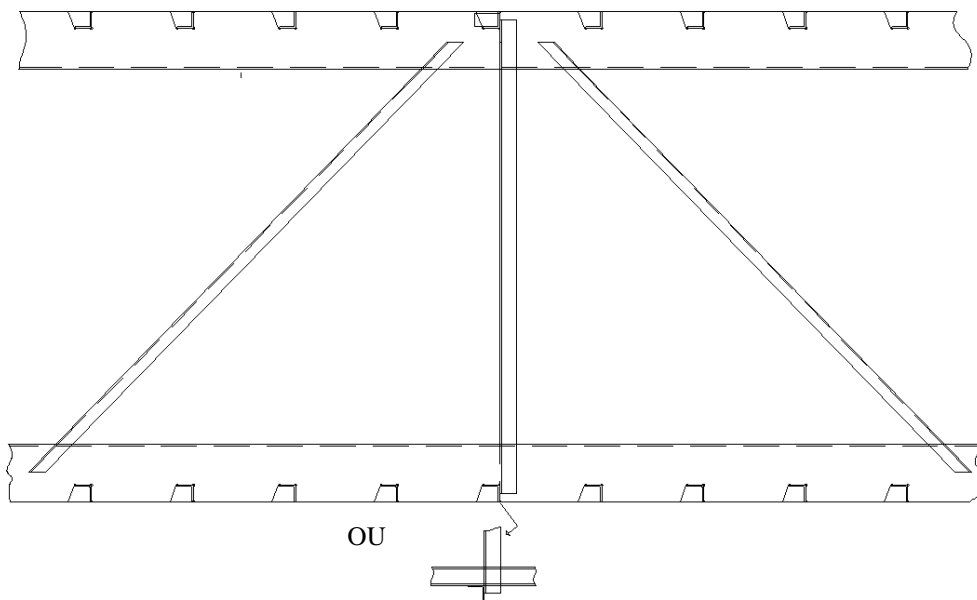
BALSAS TIPO A - SISTEMA LONGITUDINAL
